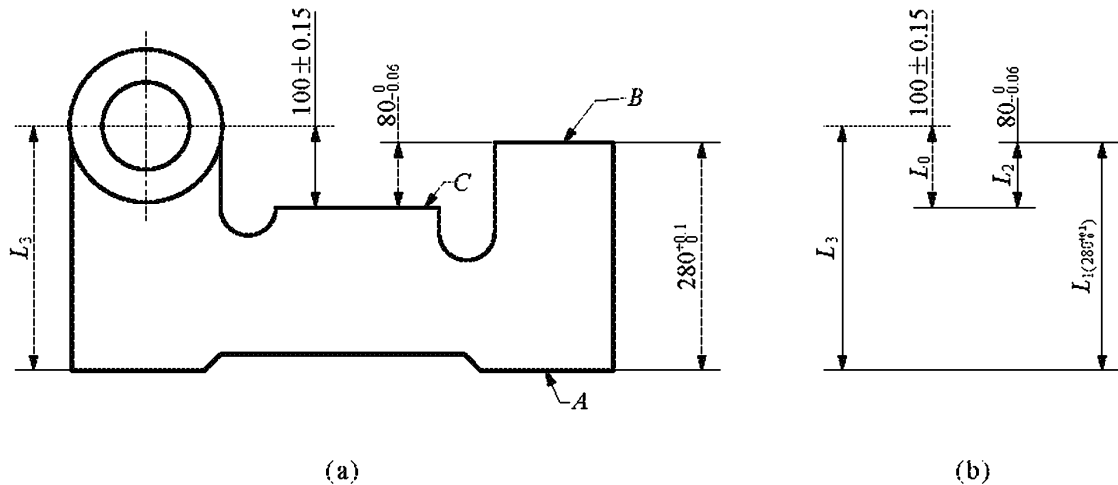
定位基准与设计基准不重合时工序尺寸的计算
